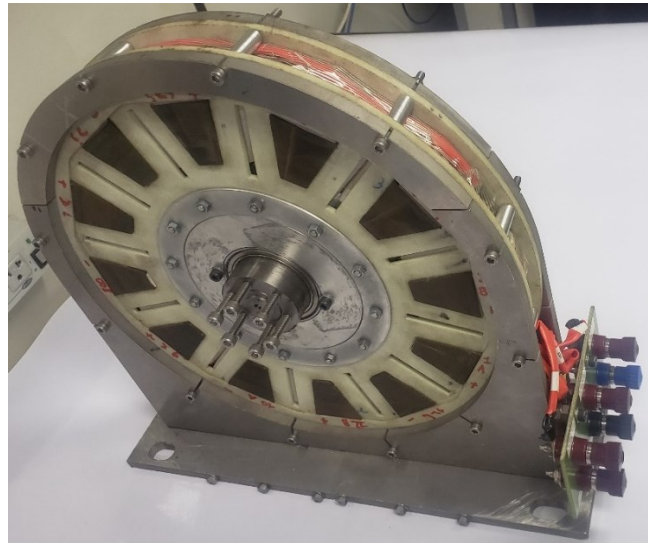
Peças que foram usinadas para o suporte dos módulos e estrutura mecânica do protótipo.
